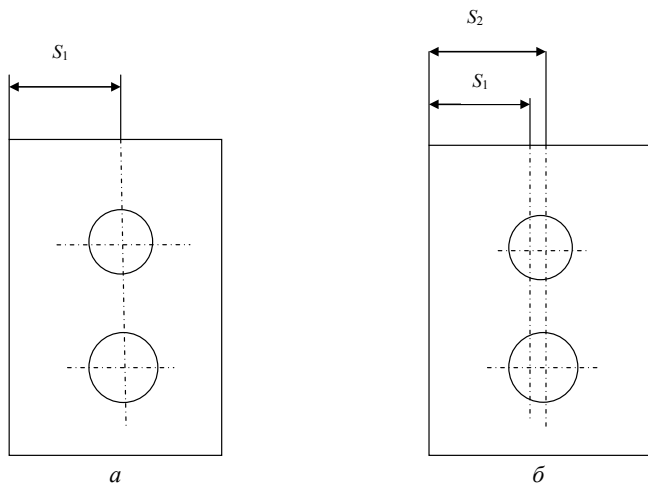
a* – размеры на чертеже детали; *б* – размеры на схеме обработки
